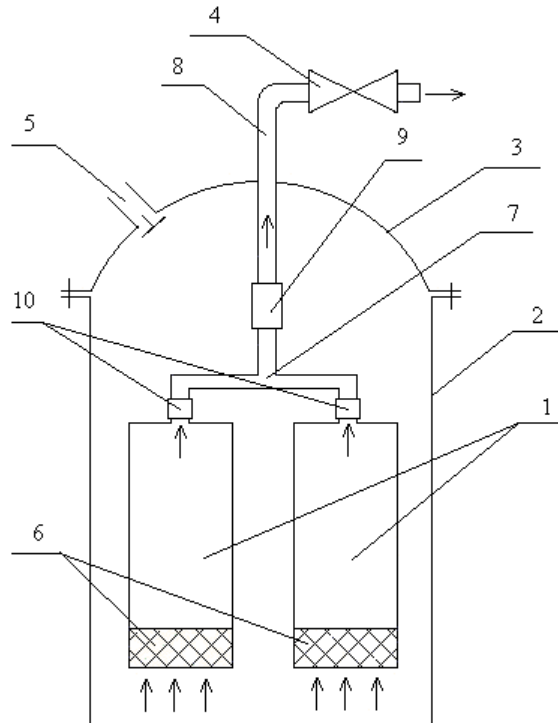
Схема порошкового огнетушителя с параллельно соединенными сосудами для ОПС: 1 – сосуды для ОПС; 2 – корпус огнетушителя; 3 – крышка корпуса огнетушителя; 4 – запорно-пусковое устройство (далее ЗПУ); 5 – заправочный штуцер с обратным клапаном; 6 – пористый материал, 7 – общий коллектор для выхода ОПС, 8 – трубка, 9 – соединительная муфта, 10 – крепления.
